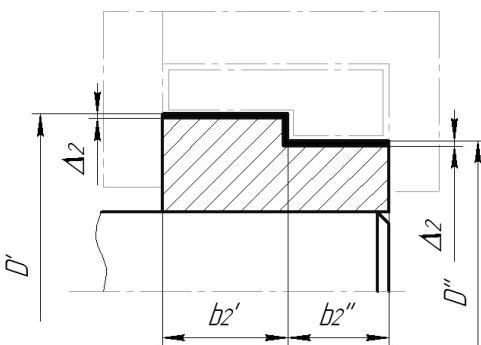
Схема нагрева в индукторе для съема детали ступенчатой формы
